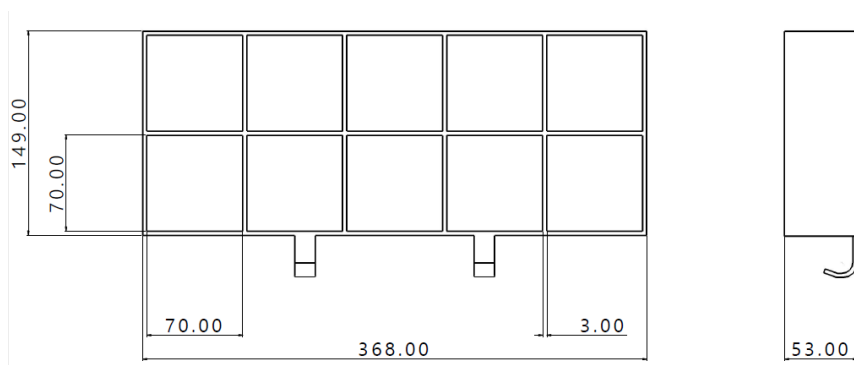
Desenho técnico do material utilizado para a separação de filtros
